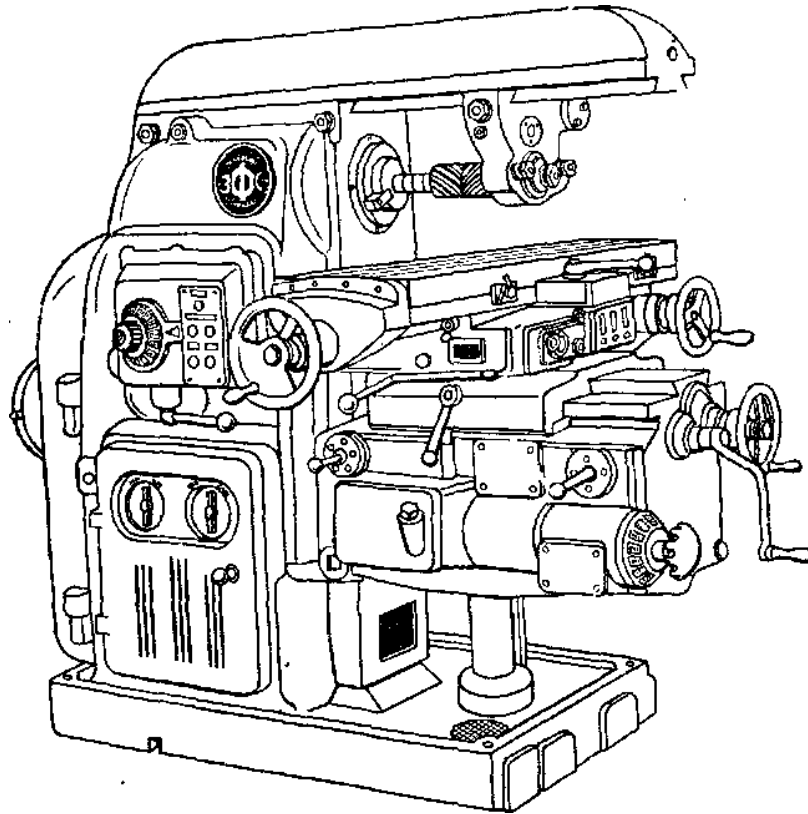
Горизонтально-фрезерний верстат 6М82Г
